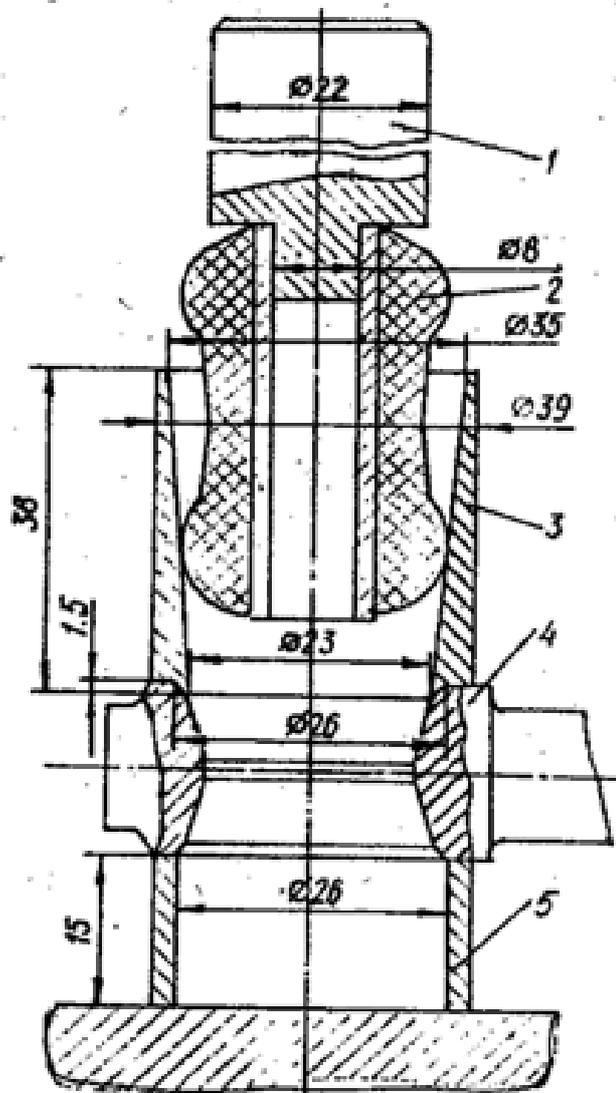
Приспособление для запрессовки резиновых шарниров в гнезда рулевых тяг: 1 - оправка; 2 - резиновый шарнир; 3 - стакан направляющий; 4 - наконечник внутренней рулевой тяги; 5 - подставка
